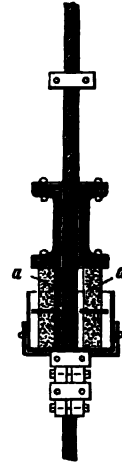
Seilbefestigung auf den Skalley-Schächten.
